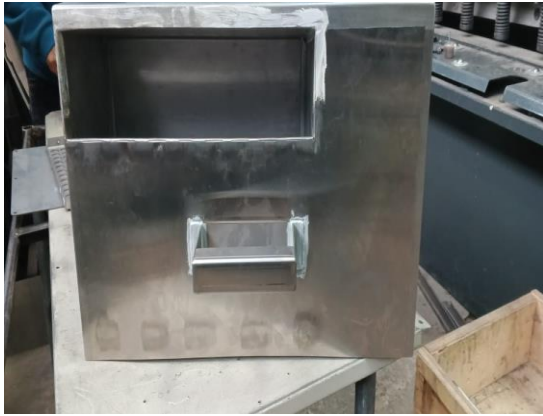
Limpieza de las partes soldadas en la estructura.
